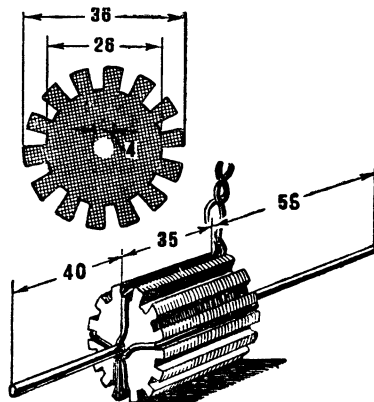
Шаблон для кружков якоря (вверху) и изготовление пакета.
